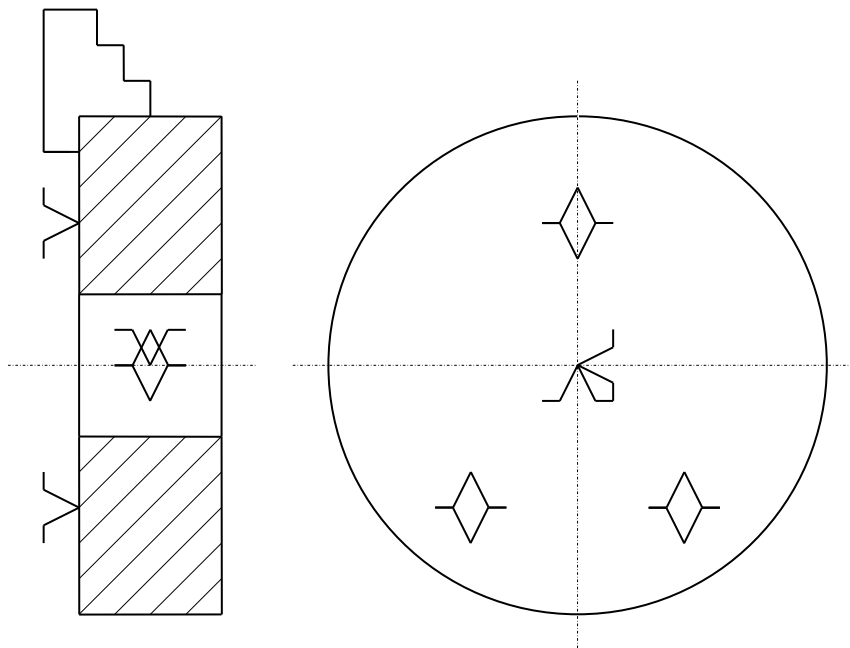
Схема базування заготовки в трикулачковому патроні
